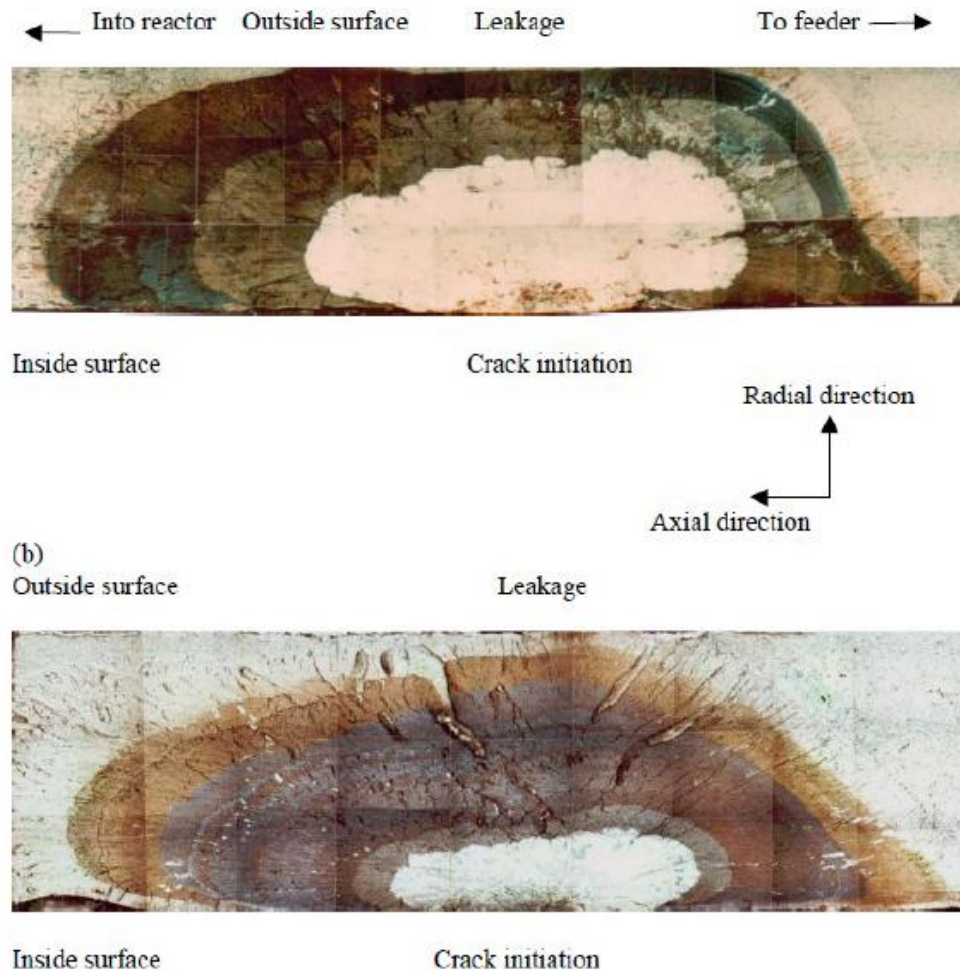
Una grieta a través de la pared en dos juntas laminadas en tubos de presión de Zr-2.5Nb en Pickering 3 (a) y Pickering 4 (b), dos centrales nucleares canadienses. Fuente: (20).
